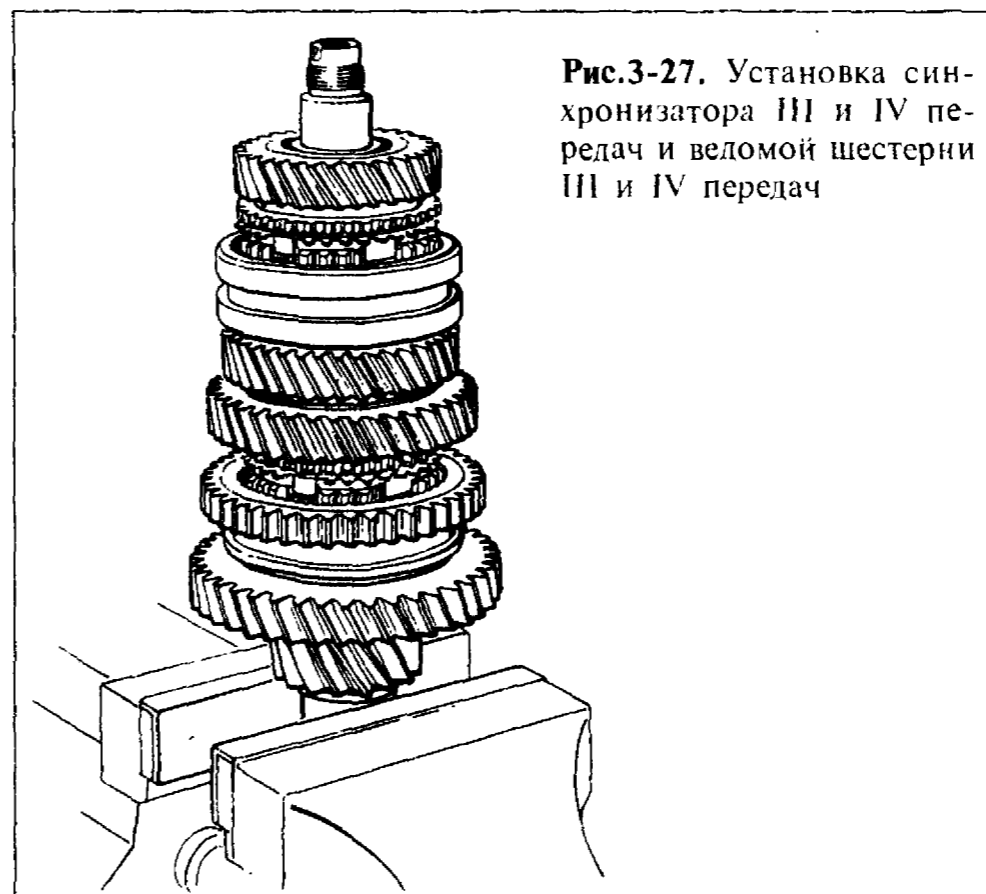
Установка синхронизатора III и IV передач и ведомой шестерни III и IV передач
